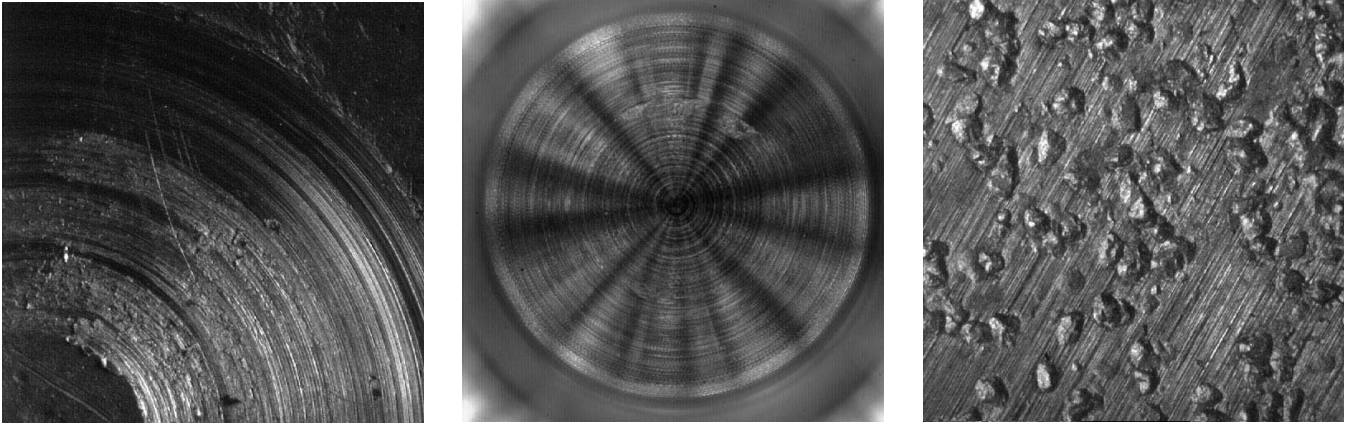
Makroskopische Aufnahmen metallischer Oberflächen: (links) Werkzeugspur; (Mitte) Membranoberfläche eines Drucksensors; (rechts) kugelgestrahlte Oberfläche.
